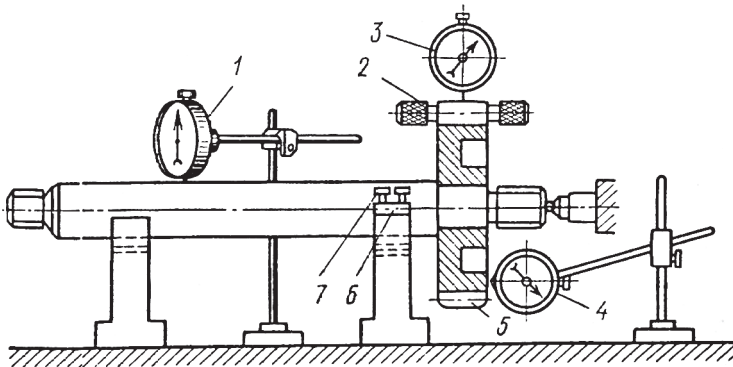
Контроль качества сборки вала с зубчатым колесом
